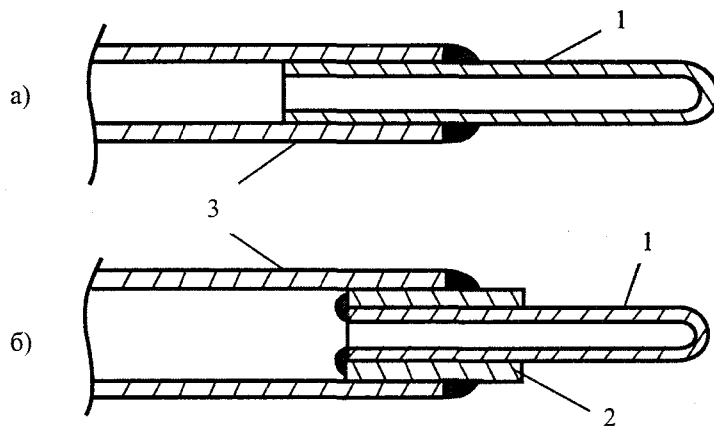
Варианты изготовления диффузионного элемента: 1 – палладиевая трубка; 2, 3 – коллекторы из нержавеющей стали
